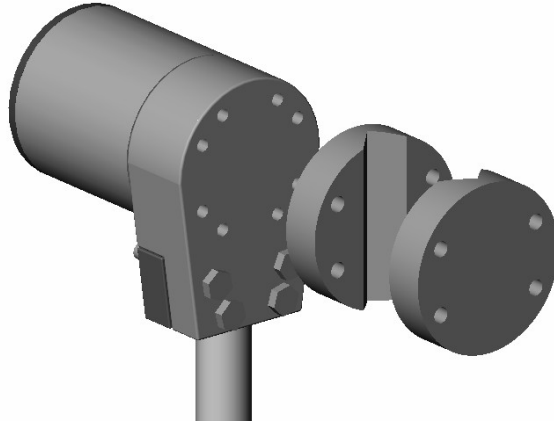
Rimozione dei blocchetti di fissaggio della barra di montaggio
